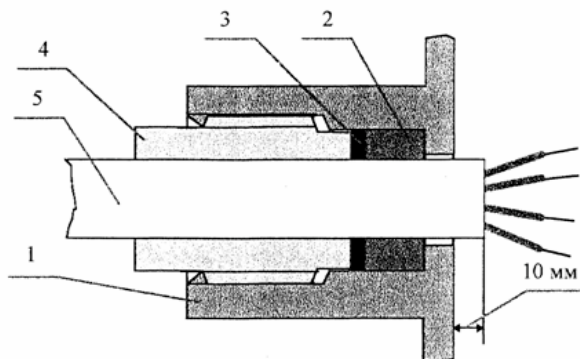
Кабельный ввод: 1 – корпус блока; 2- уплотнительное кольцо; 3 – шайба; 4 – гайка; 5 – кабель.
